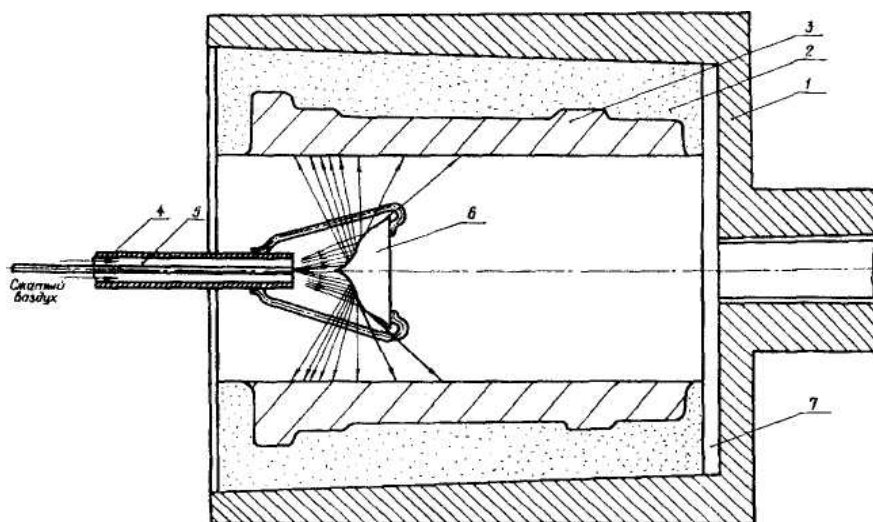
Схема вилівка гільз двигуна внутрішнього згоряння:
